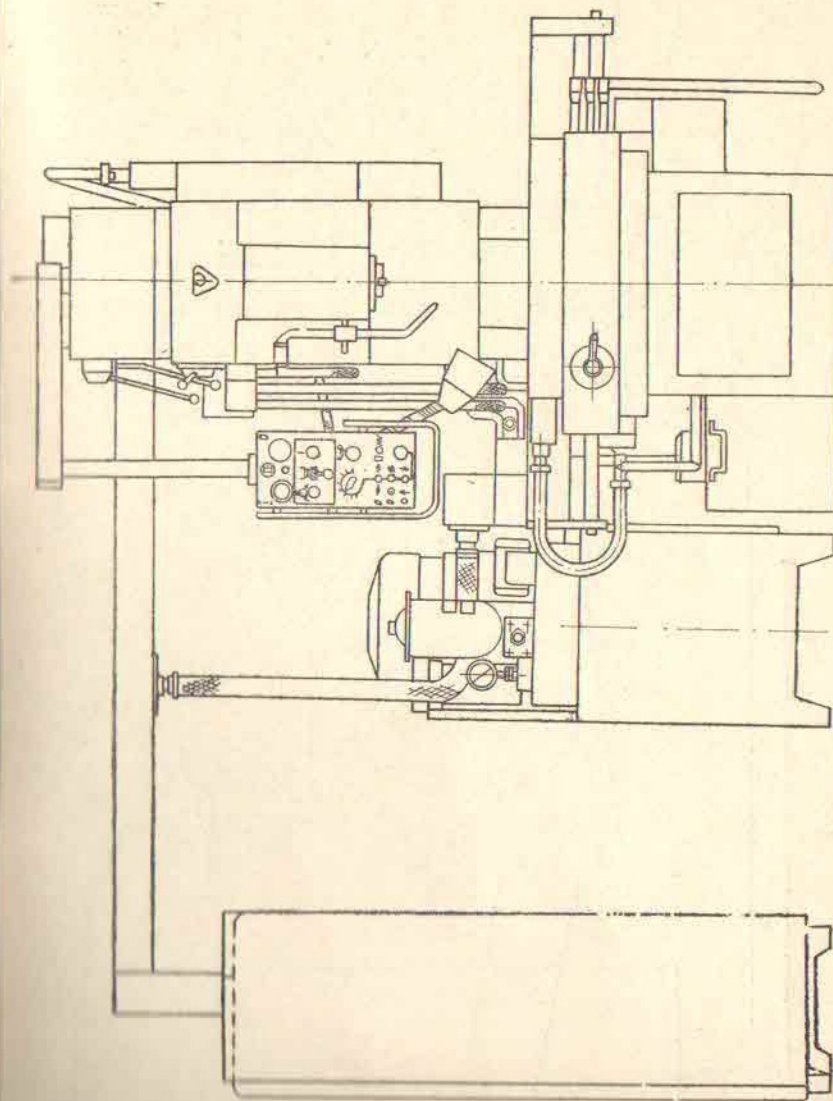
Станок вертикально-фрезерный с крестовым столом и ЧПУ модели 6520Ф3-36.
